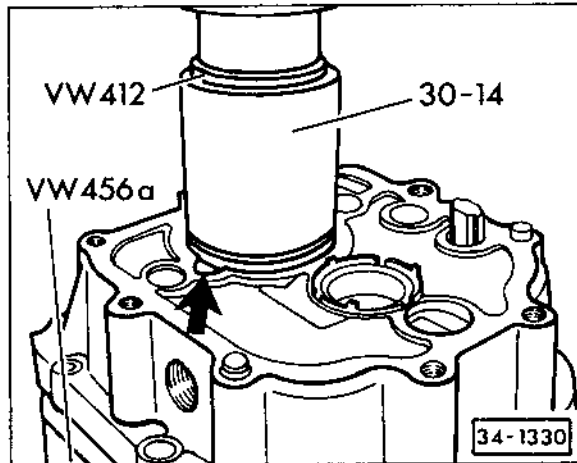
Rillenkugellager bis Anschlag in Lagerschild einpressen.
